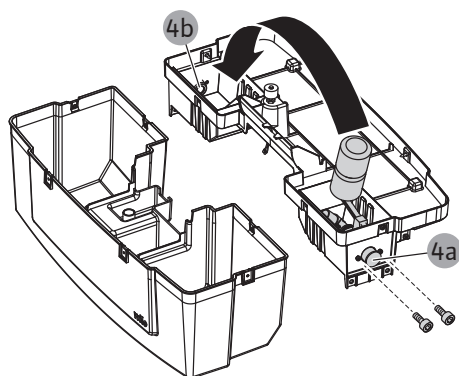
Retrait du couvercle de la bache de stockage et desserrage des vis de fixation de la vanne de réalimentation
